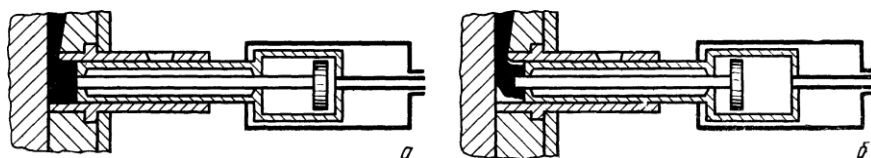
Схема двойного прессования («Acurad-процесс»):
